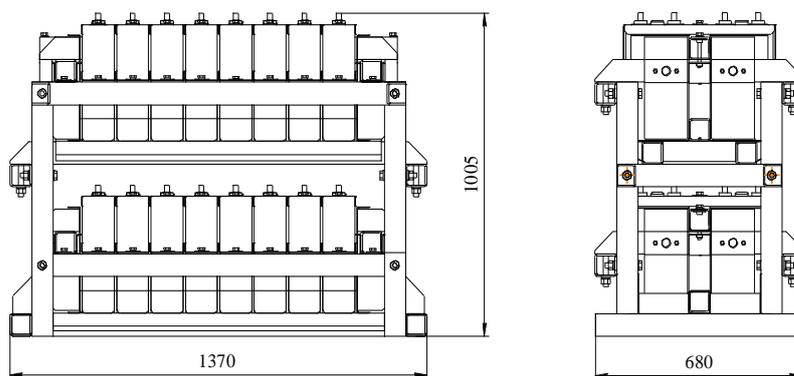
Габаритный чертеж СА-У1
